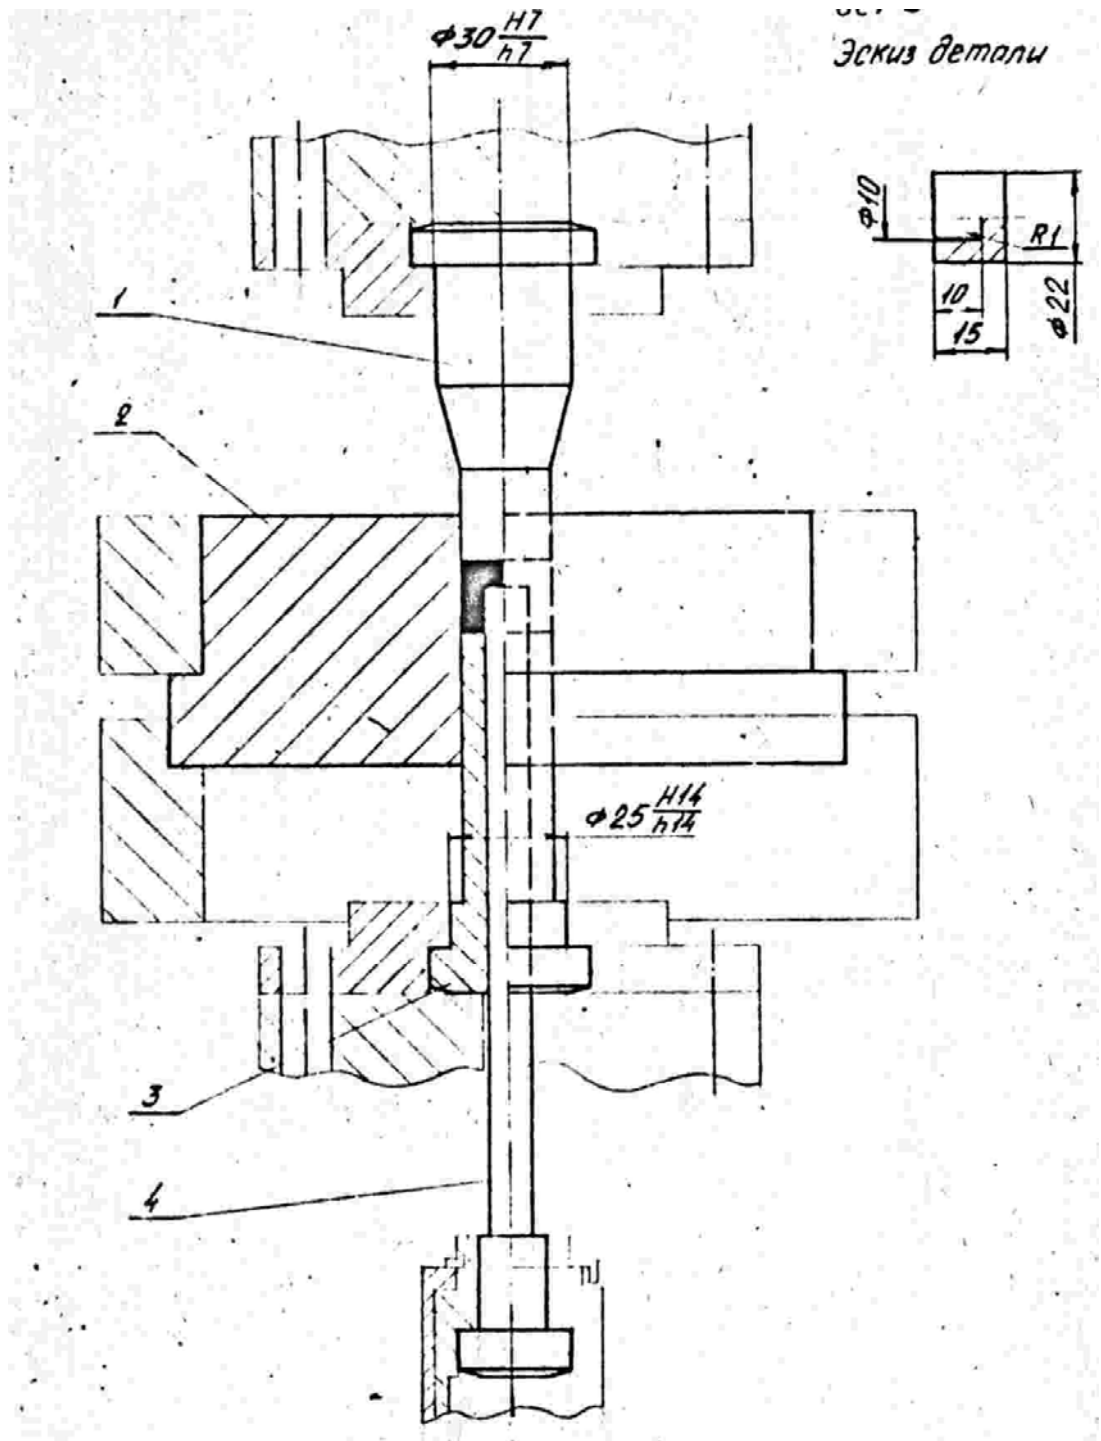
Конструкция рабочих частей пресс-форм (матрица, пуансон, стержень) для прессования изделия цилиндрической формы с внутренним отверстием и буртом
